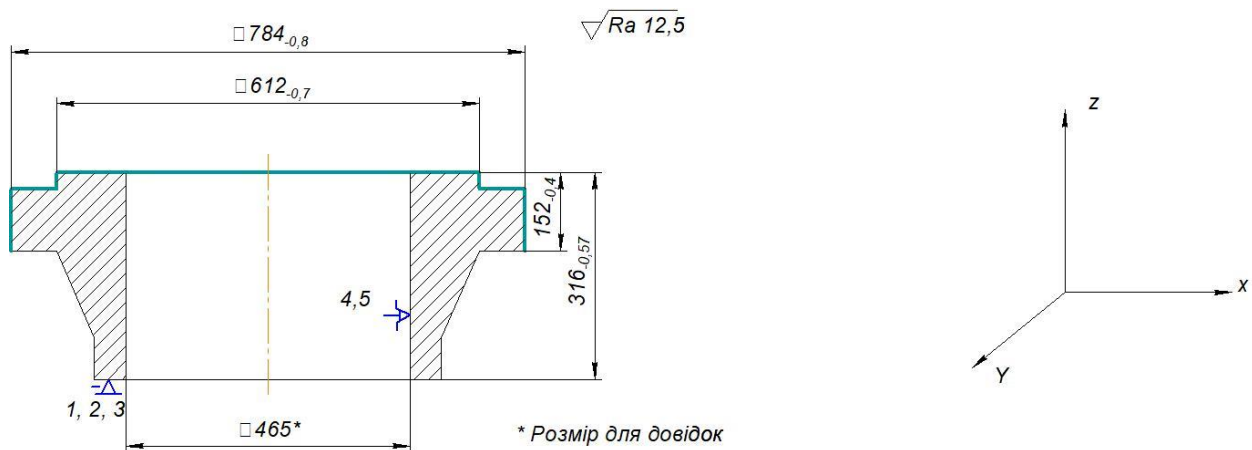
Схема базування заготовки на токарно-гвинторізній операції 030
